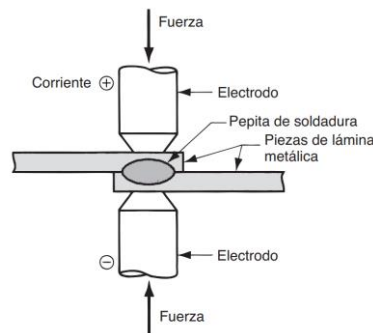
Principales componentes del proceso de soldadura de puntos por resistencia [15]
